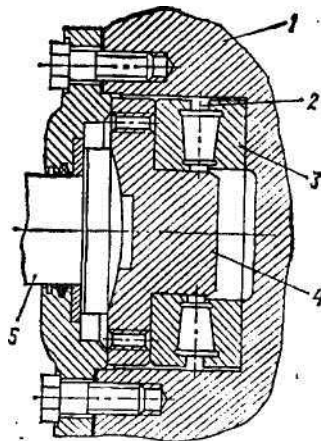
Вузол упорного підшипника механізму регулювання зазору:
